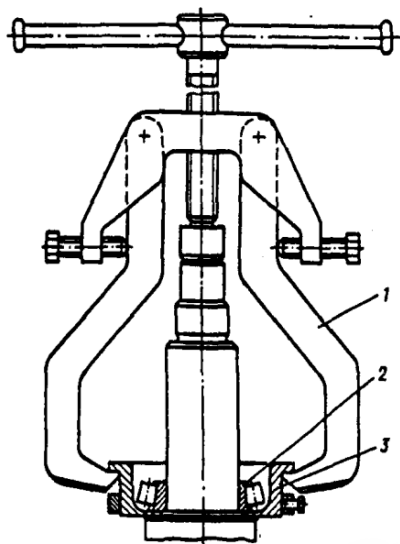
Захват для зняття внутрішнього кільця зовнішнього підшипника циліндричної шестерні середнього моста ПМ 1878-26-2: 1 – стискальні елементи; 2 – фіксатори; 3 – вал із різьбленням; 4 – ручка подачі.
